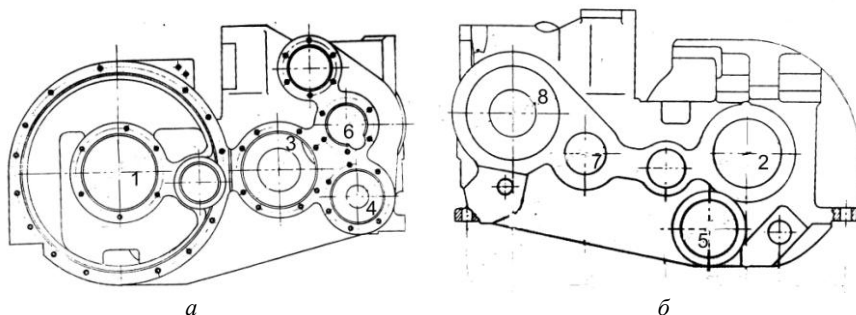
Эскиз корпуса редуктора из сплава АК6Мг:
